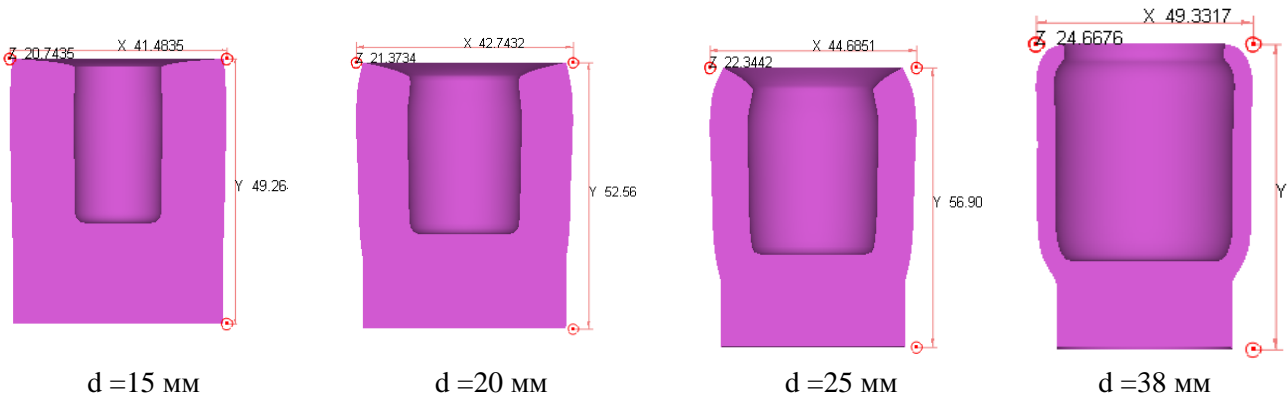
Кінцева форма виробу з розмірами, що були отримані (початкова висота розташування заготовки $h=5$ мм (див. рис. 1а))
